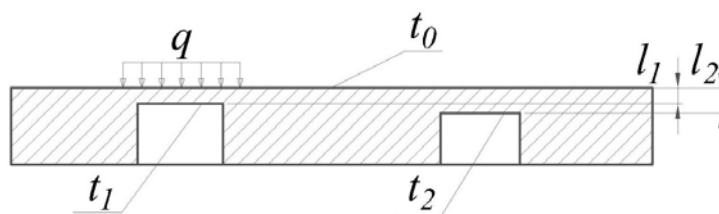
Схема для определения температуры на поверхности резания обрабатываемой заготовки
